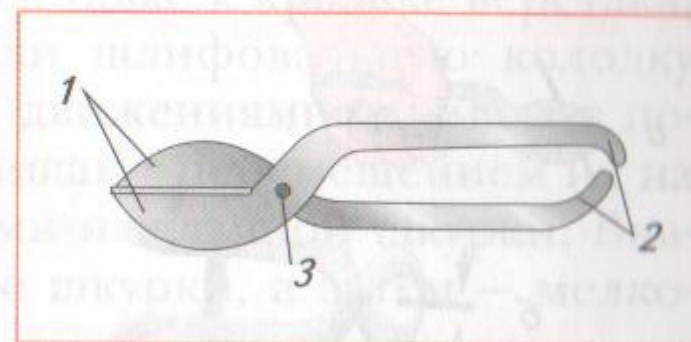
Ножницы слесарные: *1* — ножи (лезвия); *2* — ручки; *3* — шарнир
